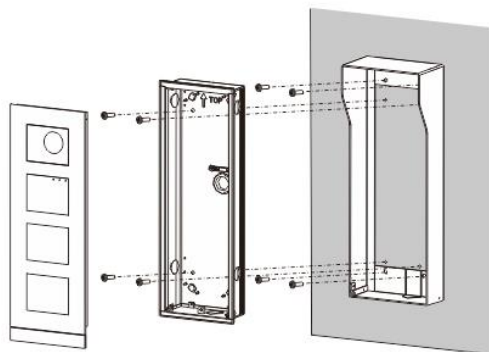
Montaggio a parete con copertura di protezione contro la pioggia
